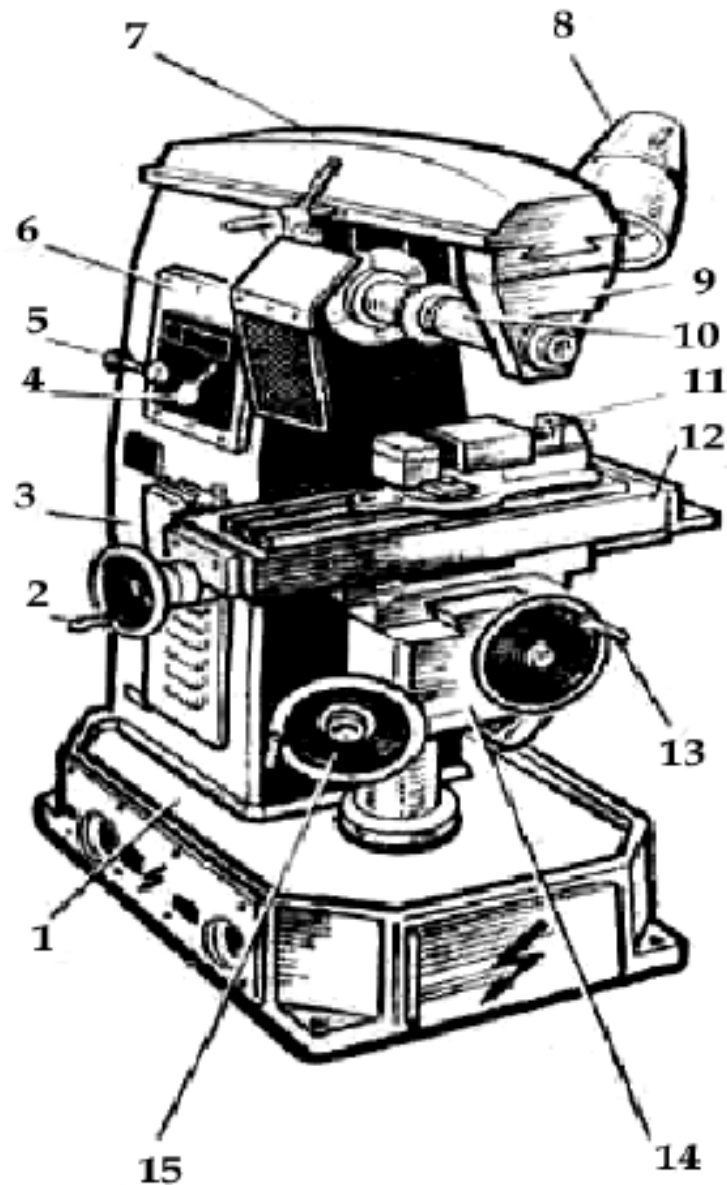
Загальний вигляд настільного горизонтально-фрезерного верстата моделі НГФ-110Ш4 1 – основа; 2 – маховик поздовжньої подачі; 3 – станина; 4, 5 – рукоятки переключення частот обертання шпинделя; 6 – коробка швидкостей; 7 – хобот; 8 – світильник; 9 – серга; 10 – оправка з фрезою; 11 – машинні тиски; 12 – стіл для установки тисків з деталлю; 13 – маховик поперечної подачі; 14 – консоль; 15 – маховик вертикальної подачі
